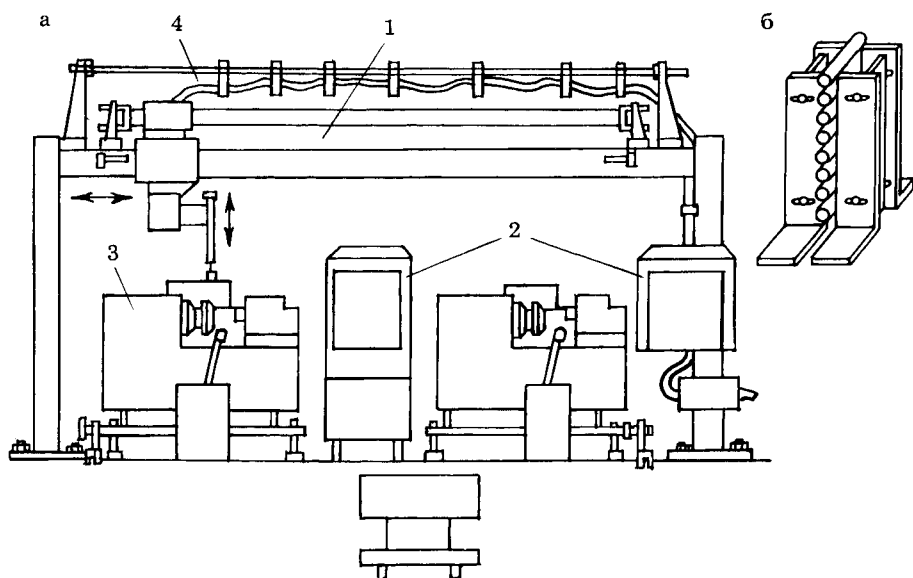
РТК с роботом портального типа (а) и конструкция кассеты с заготовками (б) для токарной обработки.
